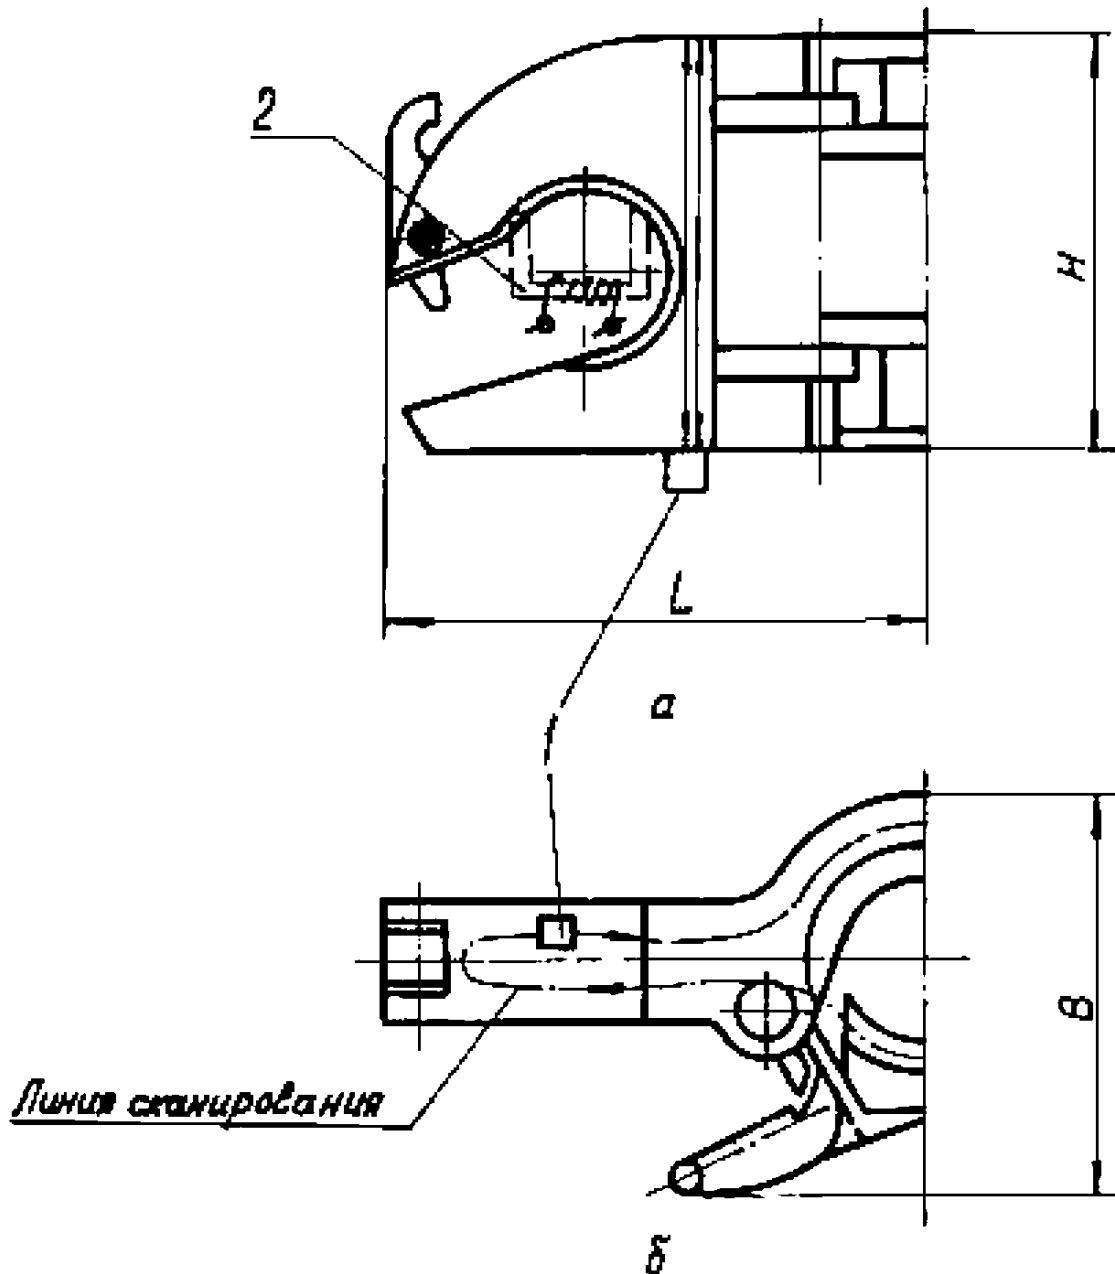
Схема катрицы адватором магнитопорошковым (а)
